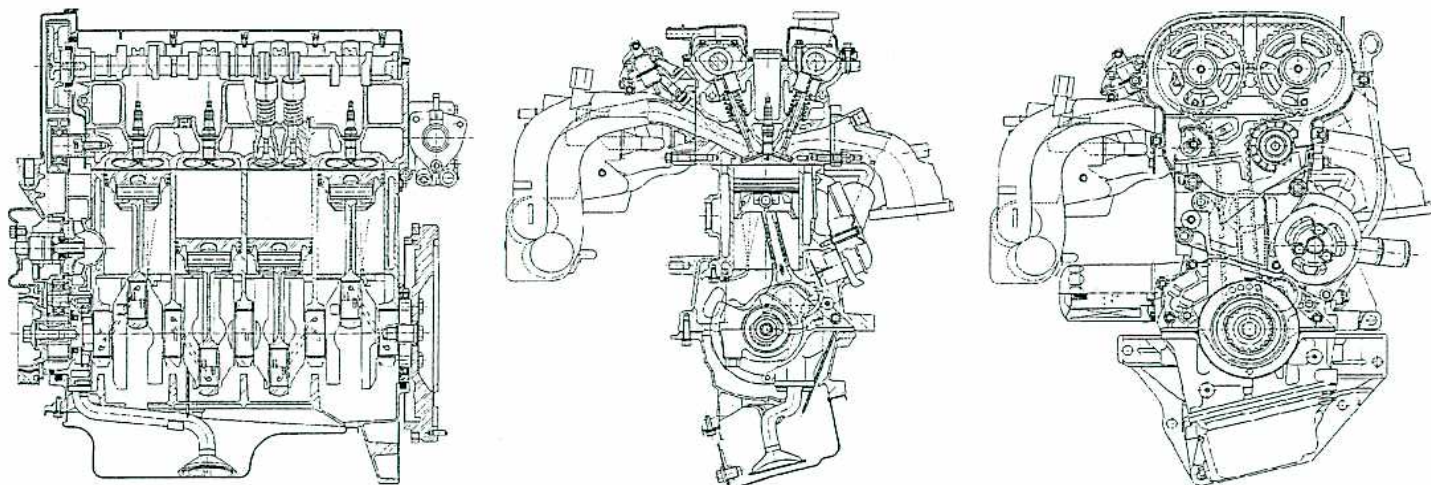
Längsschnitt, Querschnitt und Frontansicht des 2,0-l-Motors
